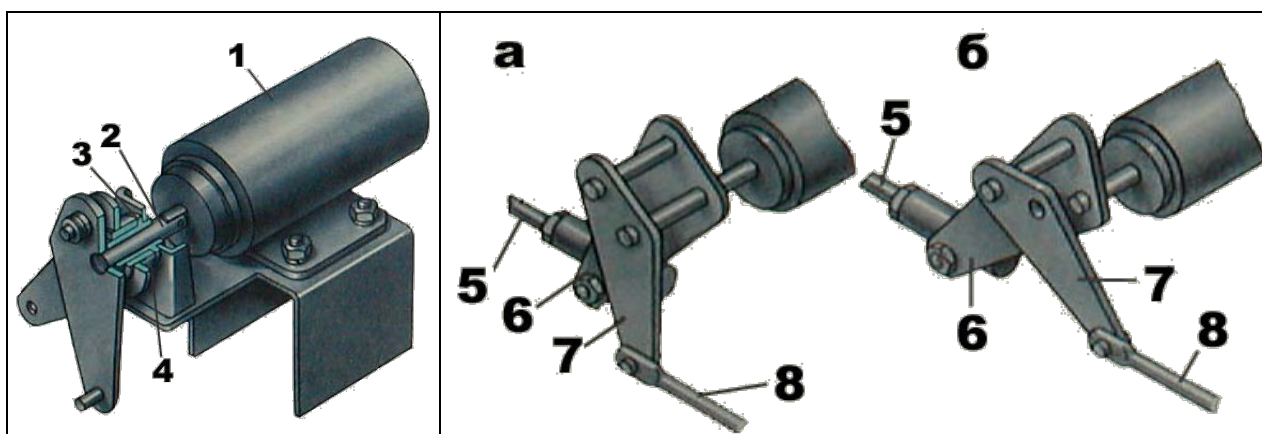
ОК-9 – Положения рукоятки привода остановки двигателя
